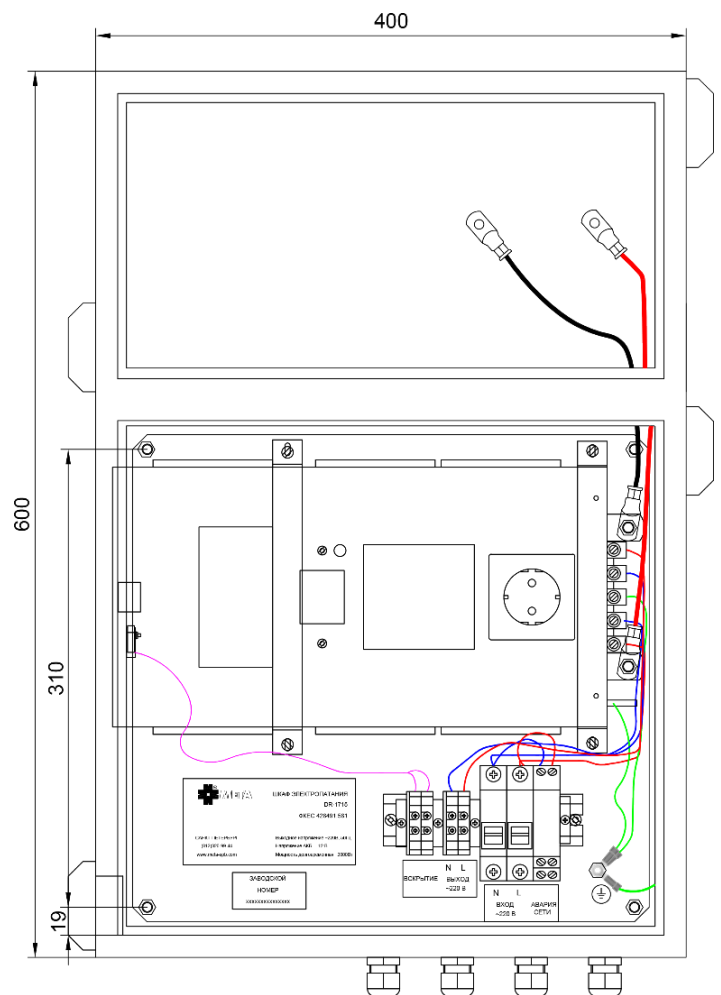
Внешний вид и габаритные размеры ШЭ DR 1715.
